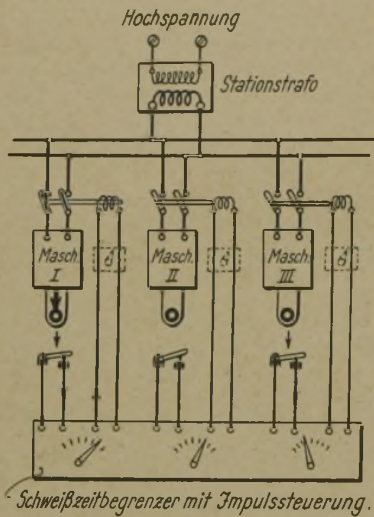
Elektrische Punktschweißung, Stromsteuerung mehrerer Maschinen
